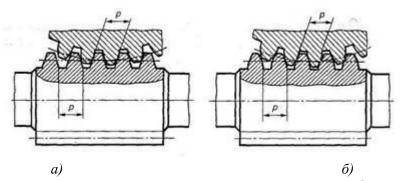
Конструкции цилиндрических червяков: a — архимедов; δ — эвольвентный
